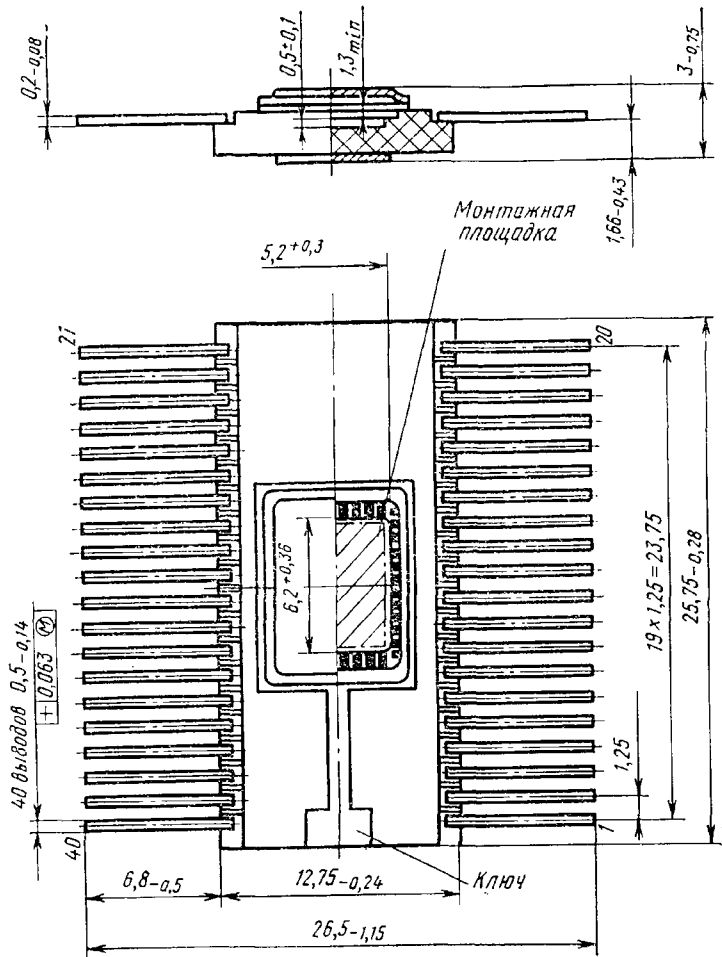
Конструкция металлокерамического корпуса 4122.40-2
